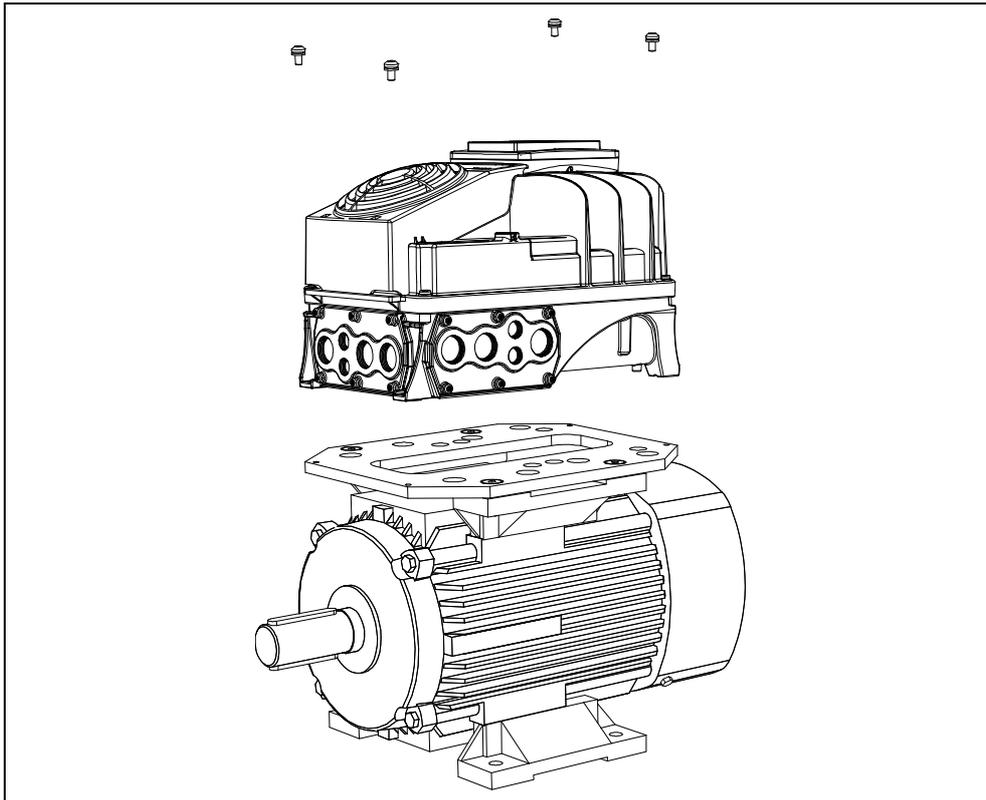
Den Frequenzumrichter am Flanschadapter mit Hilfe der 4 Schrauben montieren.
